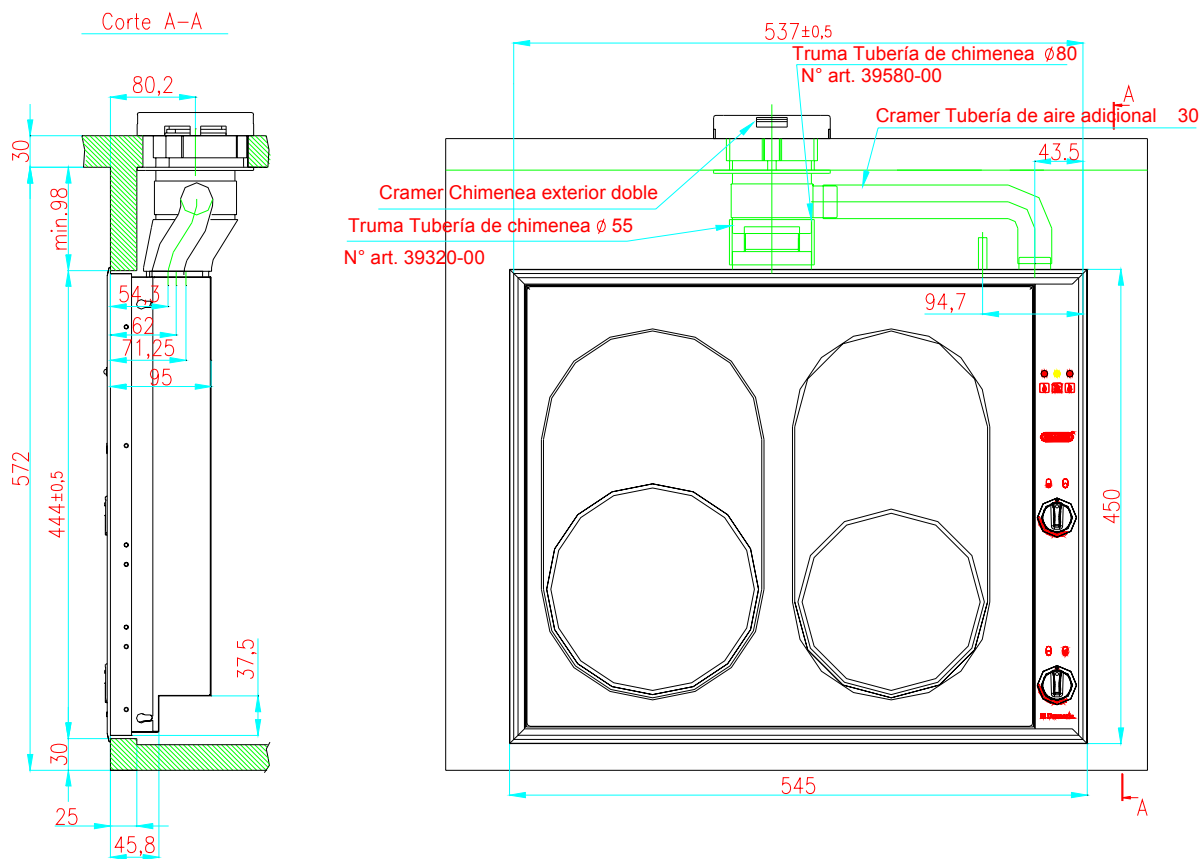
Conducto de chimenea para el escape de gas y la entrada de aire del exterior horizontal parte lateral derecha (sistema de chimenea de pared exterior ilustración 6)
